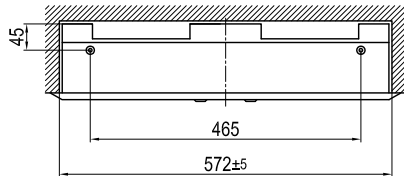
Габаритные и установочные размеры металлокорпусов
